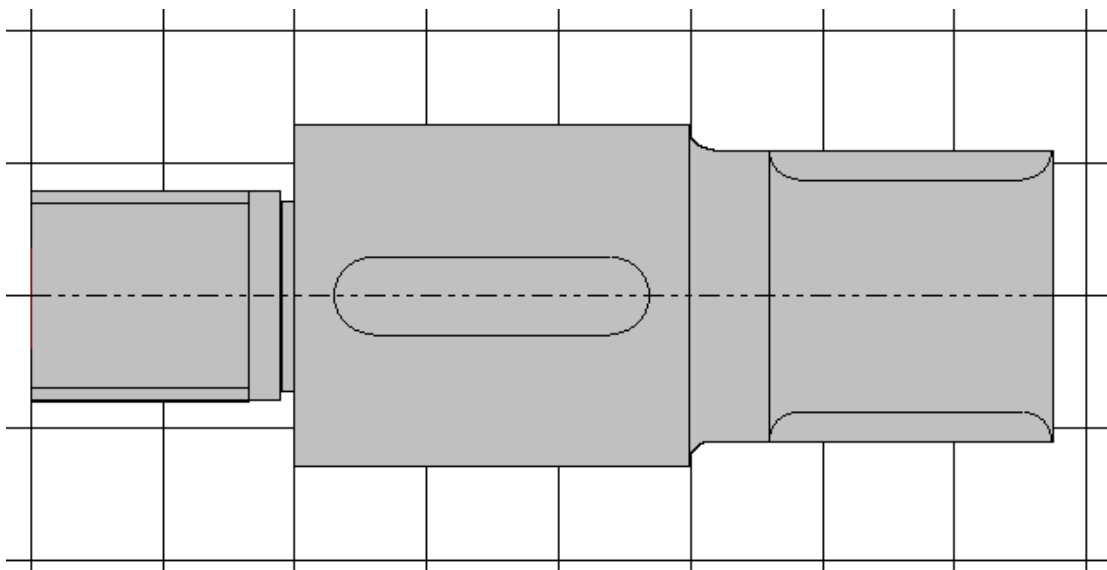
Редактор АПМ Shaft. Фрагмент вала с резьбой, шпоночным и шлицевым соединением.
